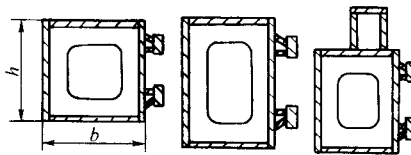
龙门式机床焊接横梁的结构断面
